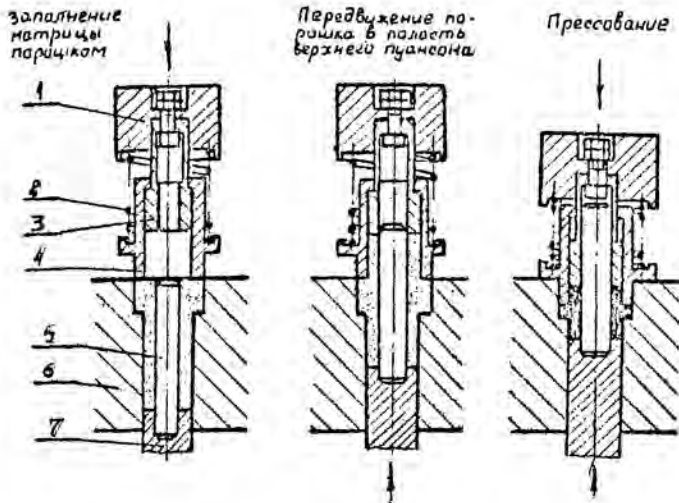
Схема автоматической прессоформы для прессования втулок с наружным буртом посередине: 1 - основание верхнего пуансона; 2 - пружина; 3 - неподвижная часть верхнего пуансона; 4 - подвижная часть верхнего пуансона; 5 - стержень; 6 - матрица; 7 - нижний пуансон
